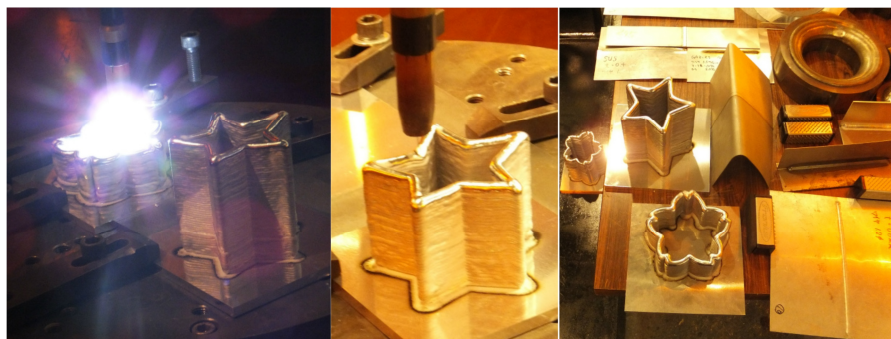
実験場での CMT 溶接、及び各種の溶接例
